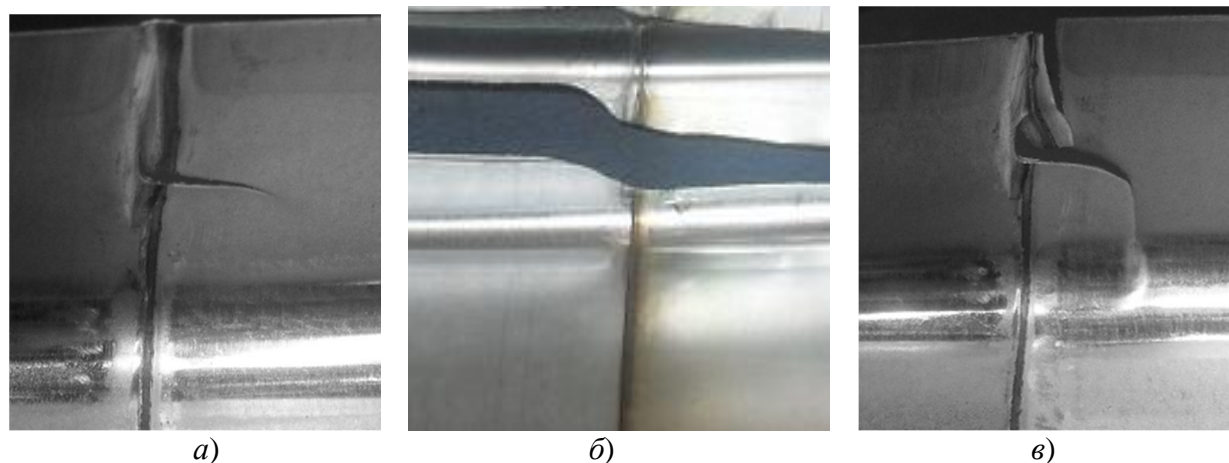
Разрывы при штамповке деталей из разнотолщинных сварных листовых заготовок
